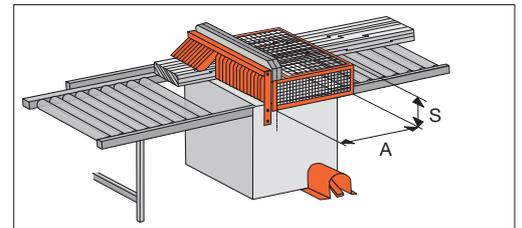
tunnel con serie di lamelle. In questo modo potete lavorare pezzi di piccole dimensioni. È necessario rispettare le distanze prestabilite per le coperture a tunnel (vedi tabella).
